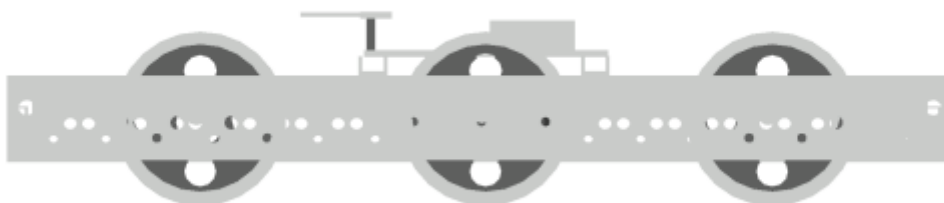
3D-модель платформы (вид сбоку)
